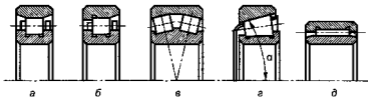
Роликовые подшипники качения: *а*, *б* – радиальные с короткими цилиндрическими роликами; *в* – радиальный сферический двухрядный; *г* – конический однорядный; *д* – игольчатый
